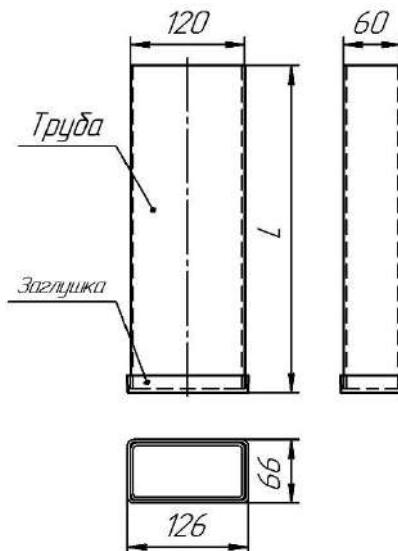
Гильза для бетонирования в фундамент, исполнение Б
